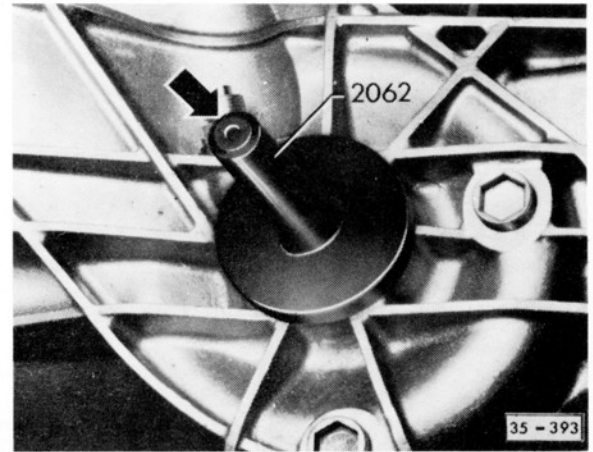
Dichtring für Flanschswelle bis Anschlag eintreiben
